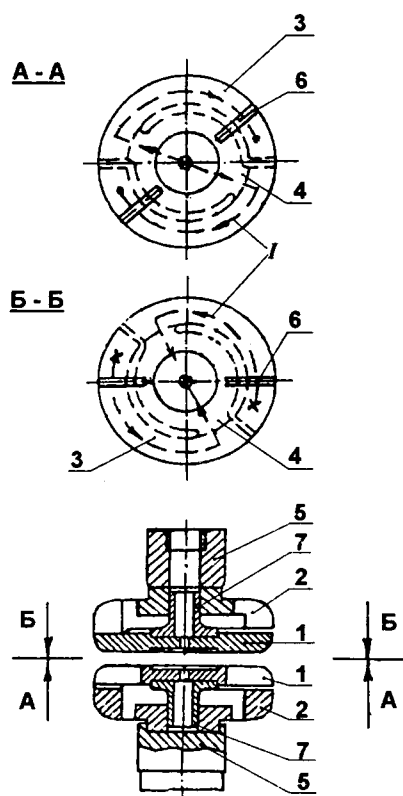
Конструкция контактов с ферромагнитными сердечниками
